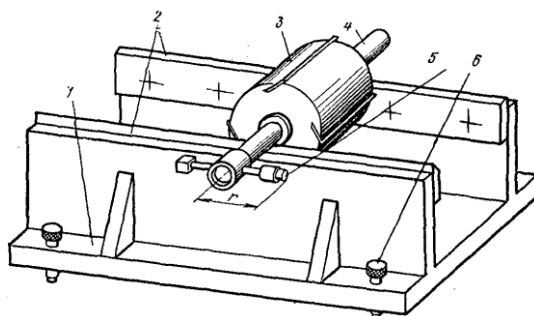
Пристосування для статичного балансування фрез: 1 — основа, 2 — ножі, 3 — ножова головка 4 — оправлення, 5 — врівноважуючий вантаж; 6 — регульована опора
